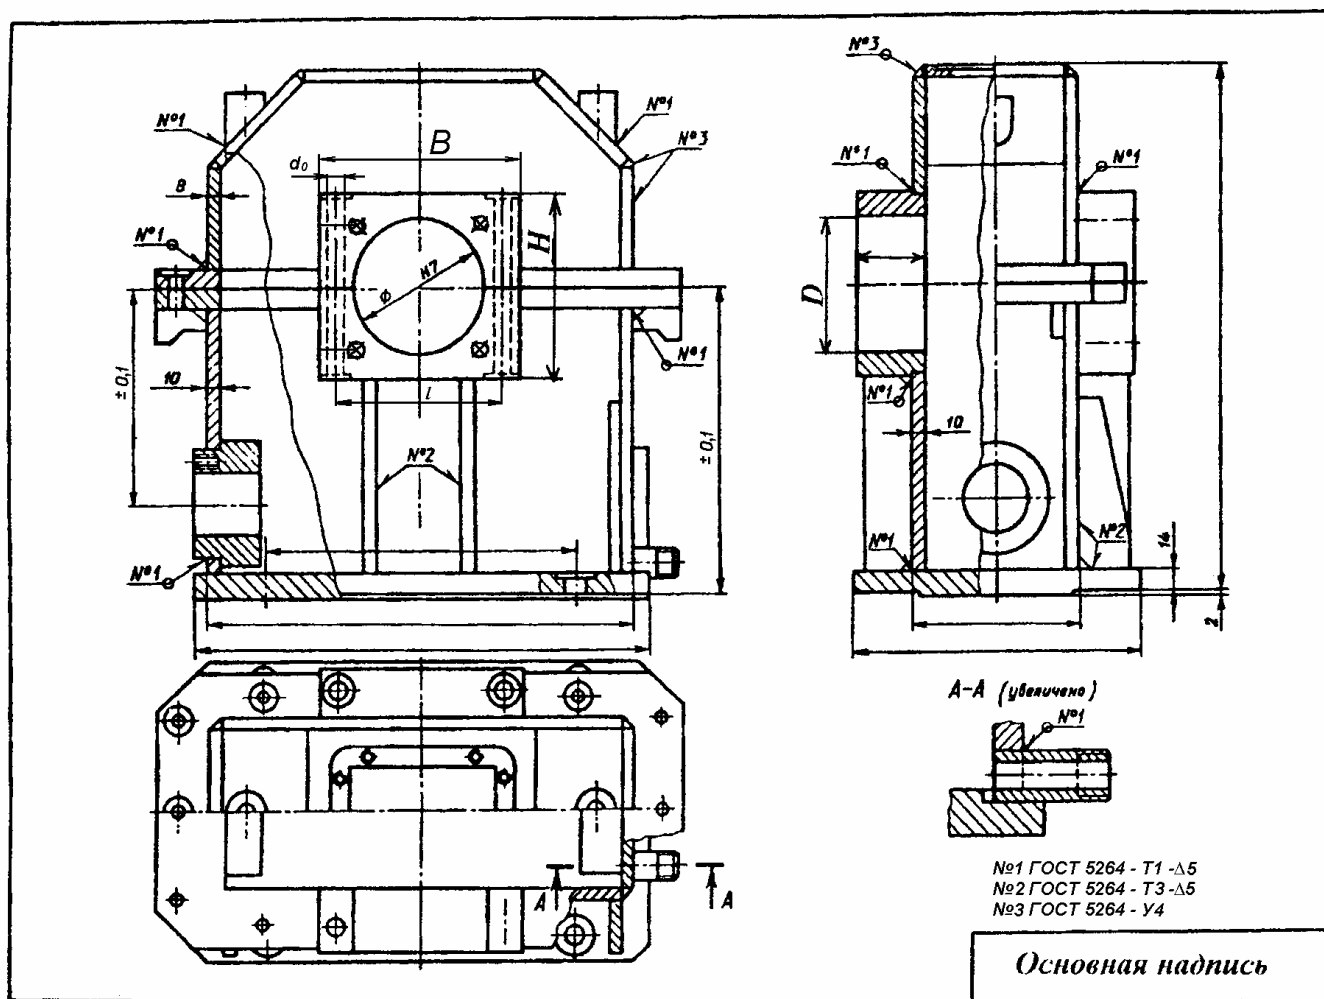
Чертеж сварного корпуса червячного редуктора
